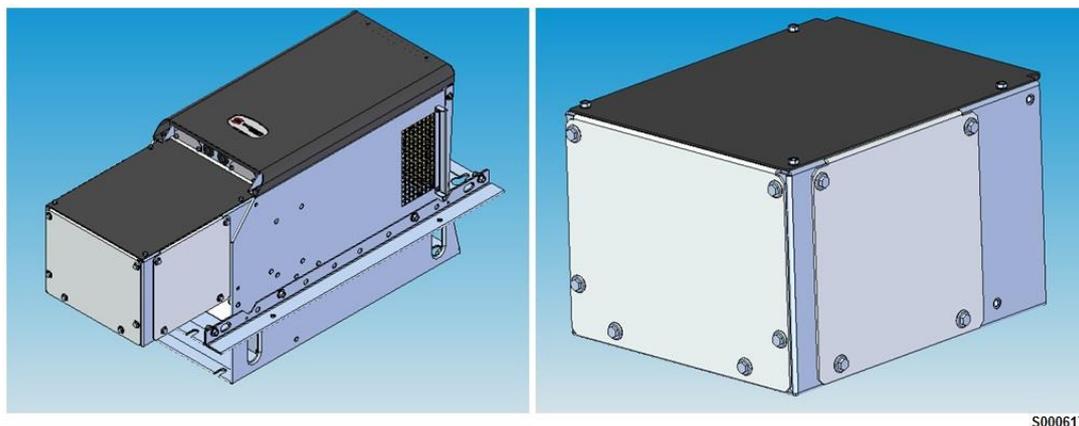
Kit di protezione NEMA 1 e installazione su SU465
